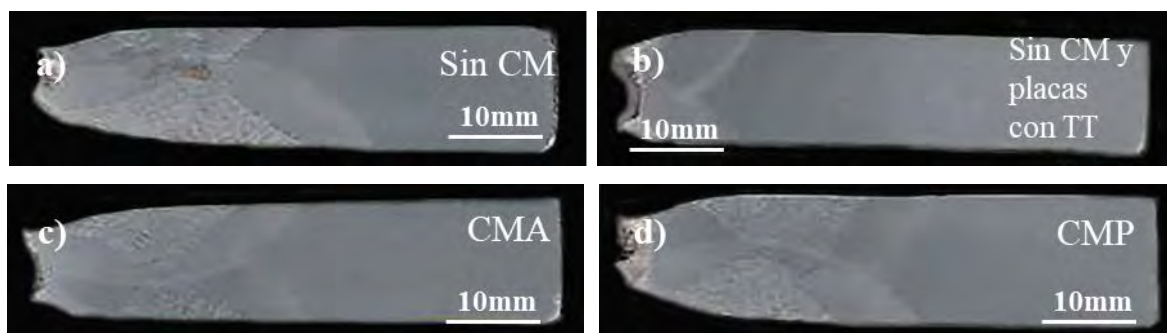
Macrografías de las fracturas de las pruebas de tensión en las soldaduras del acero API X-70; a) sin CM, b) sin CM y placas con TT, c) con CMA y d) con CMP.
